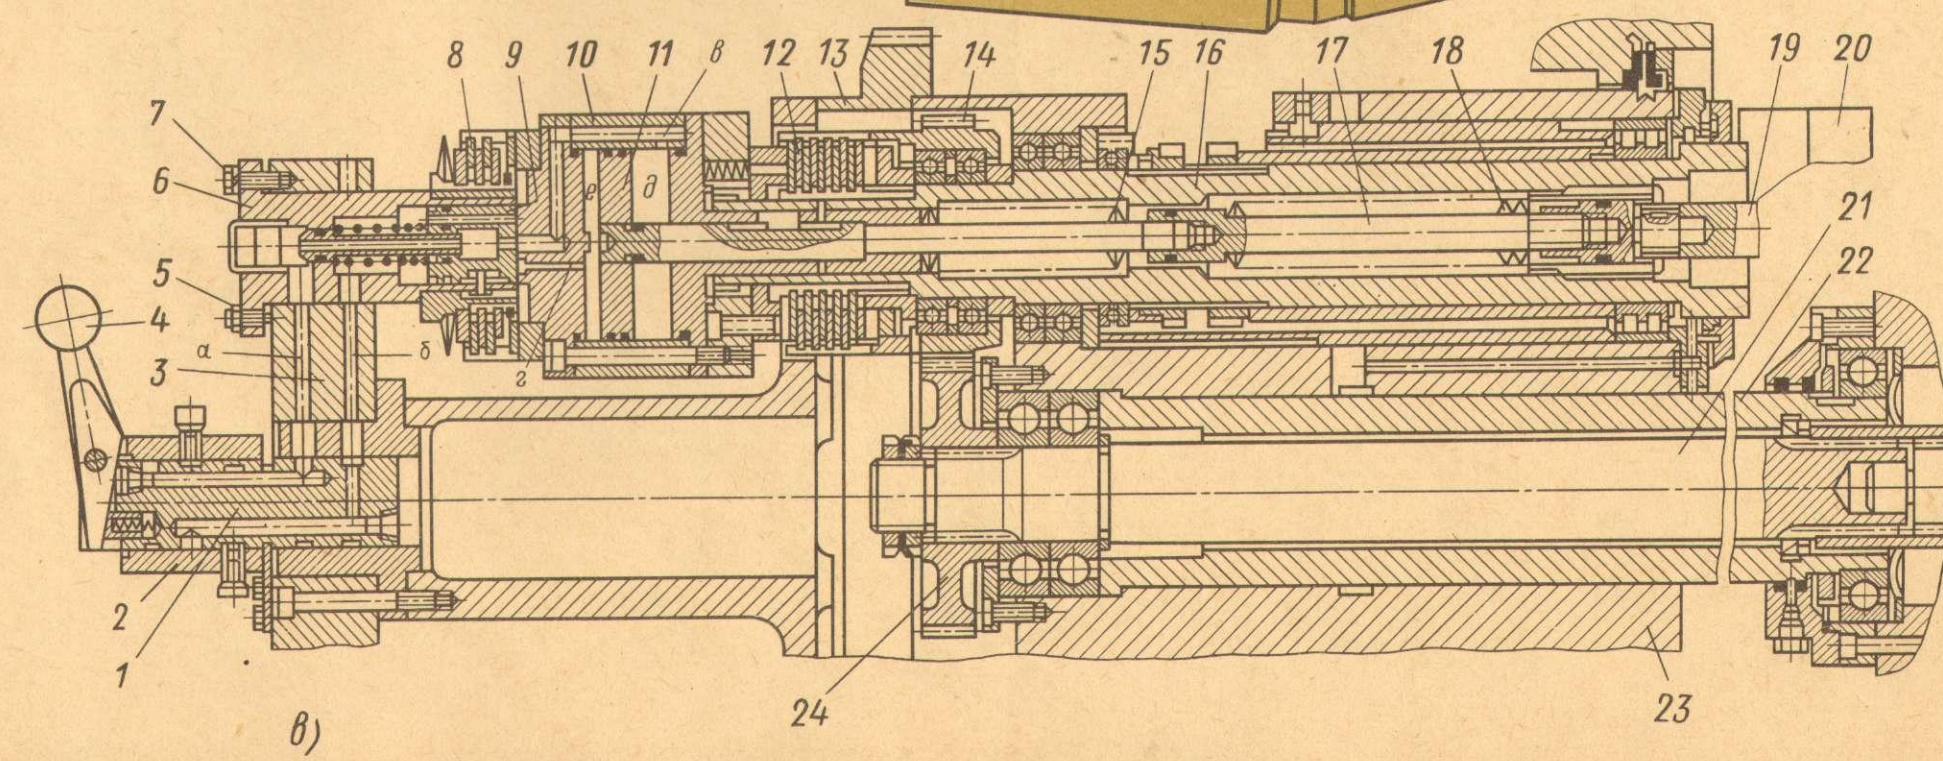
Токарный шестишпиндельный горизонтальный полуавтомат модели 1А240П-6
